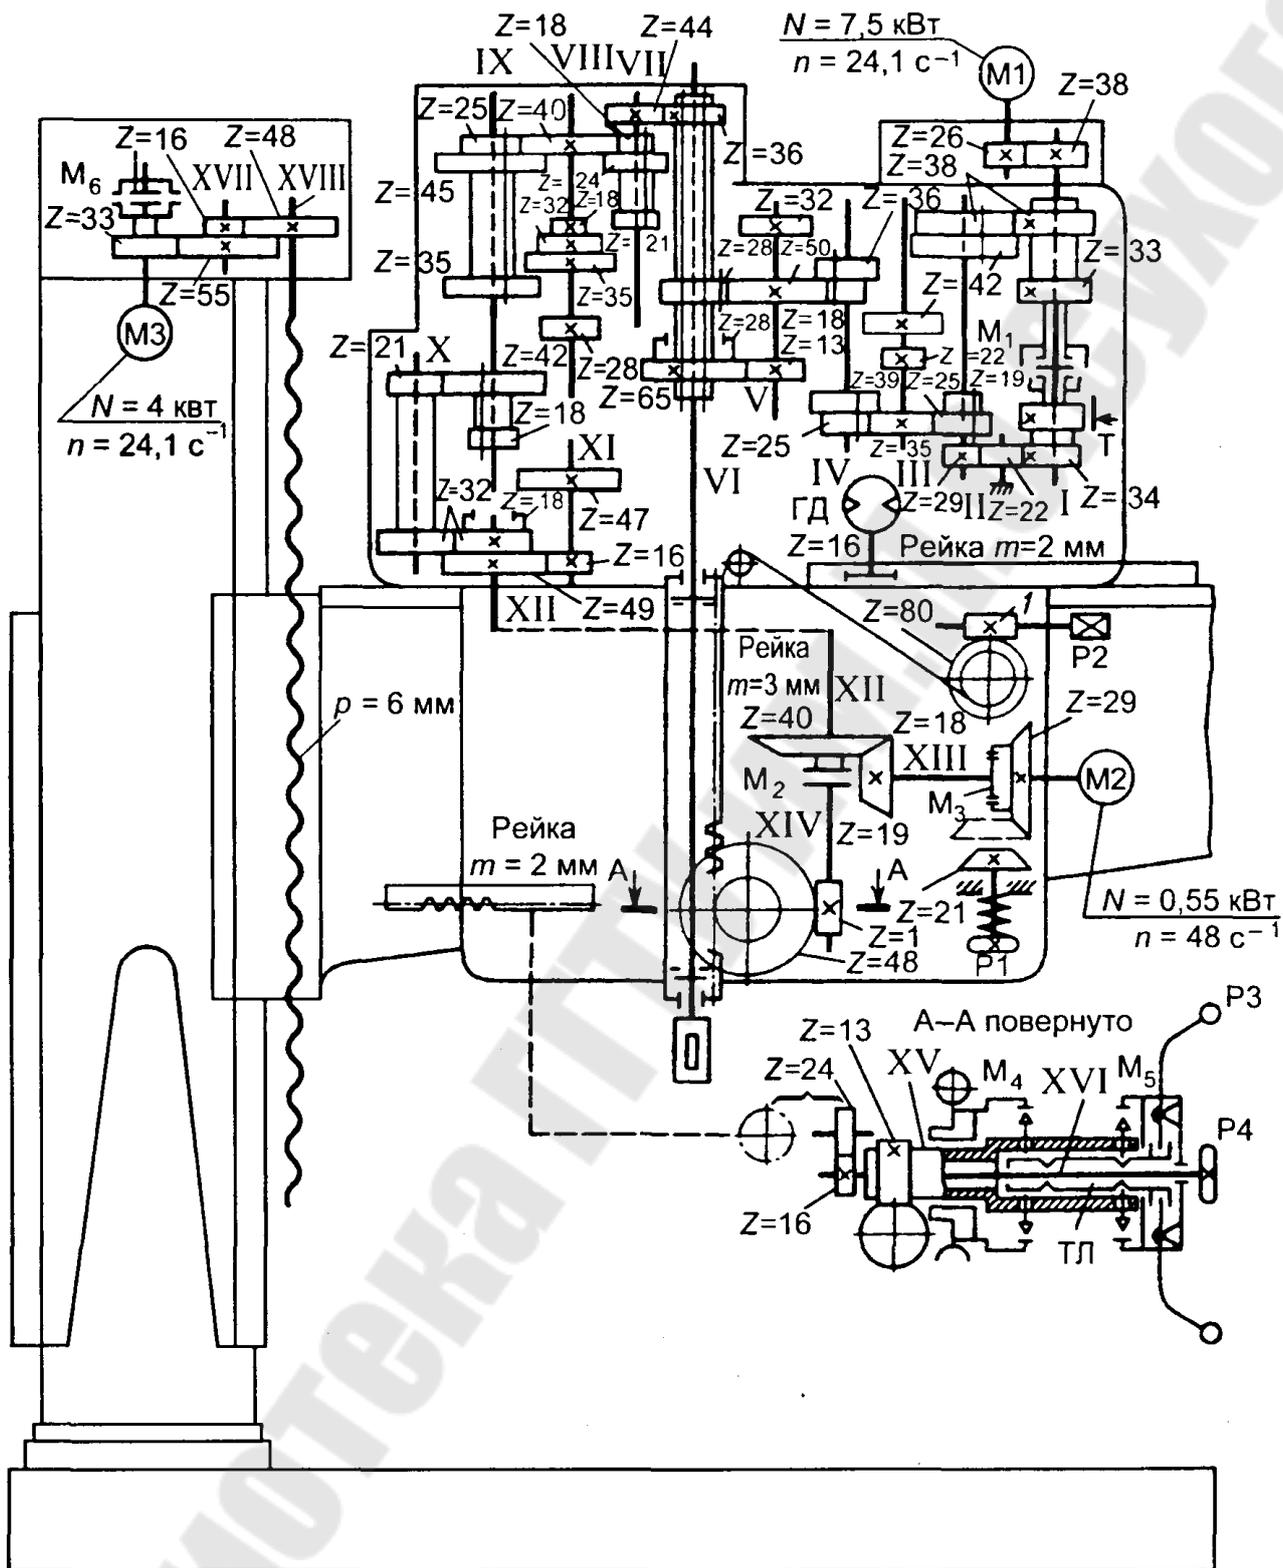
Кинематическая схема радиально-сверлильного станка
